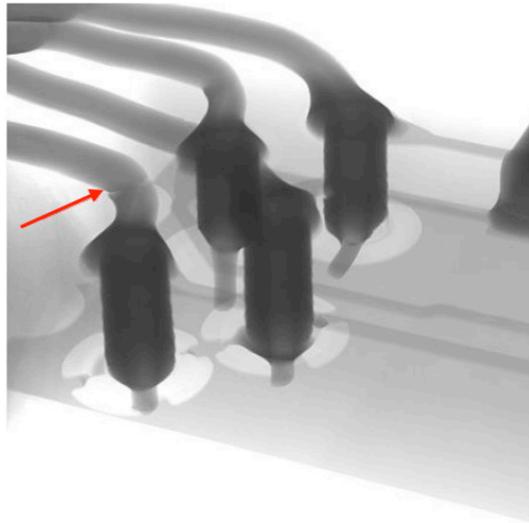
Componentes electrónicos soldados a la tablilla electrónica a mayor magnificación y con una inclinación para resaltar detalles de la fractura localizada en una de las terminales del sensor magnético soldado a la tablilla electrónica.
